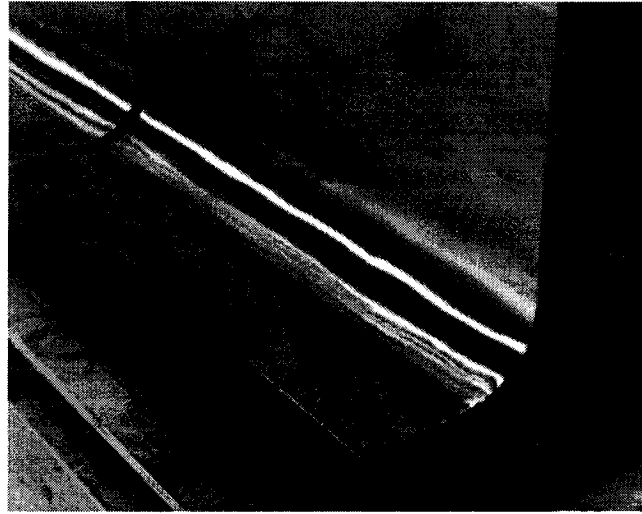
Passes de soudure sur les échantillons
